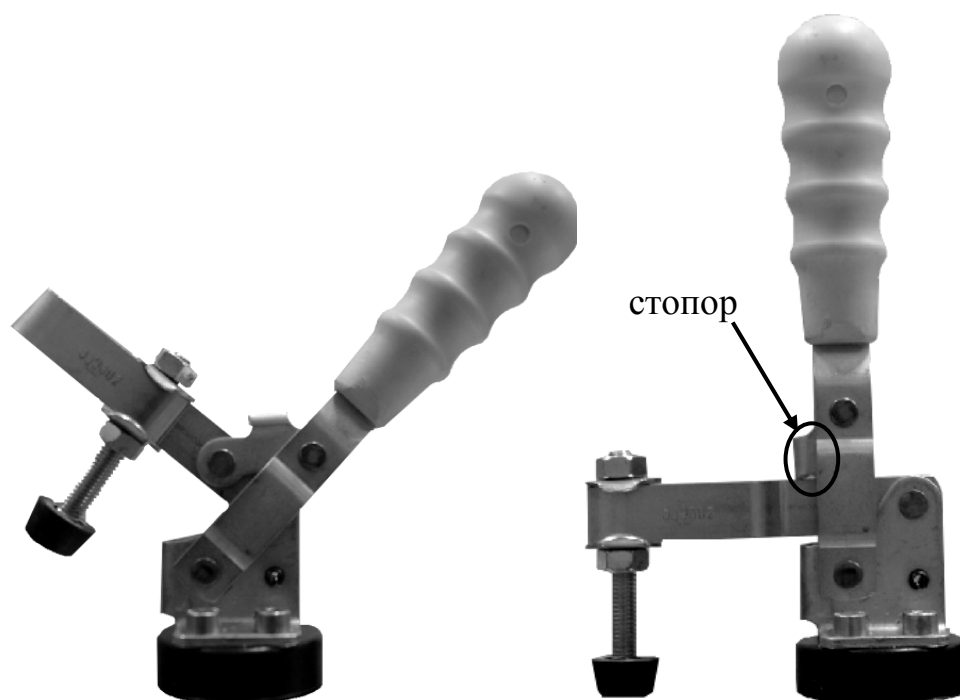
Ручной шарнирно-рычажный прижим универсального сборочно-сварочного приспособления
